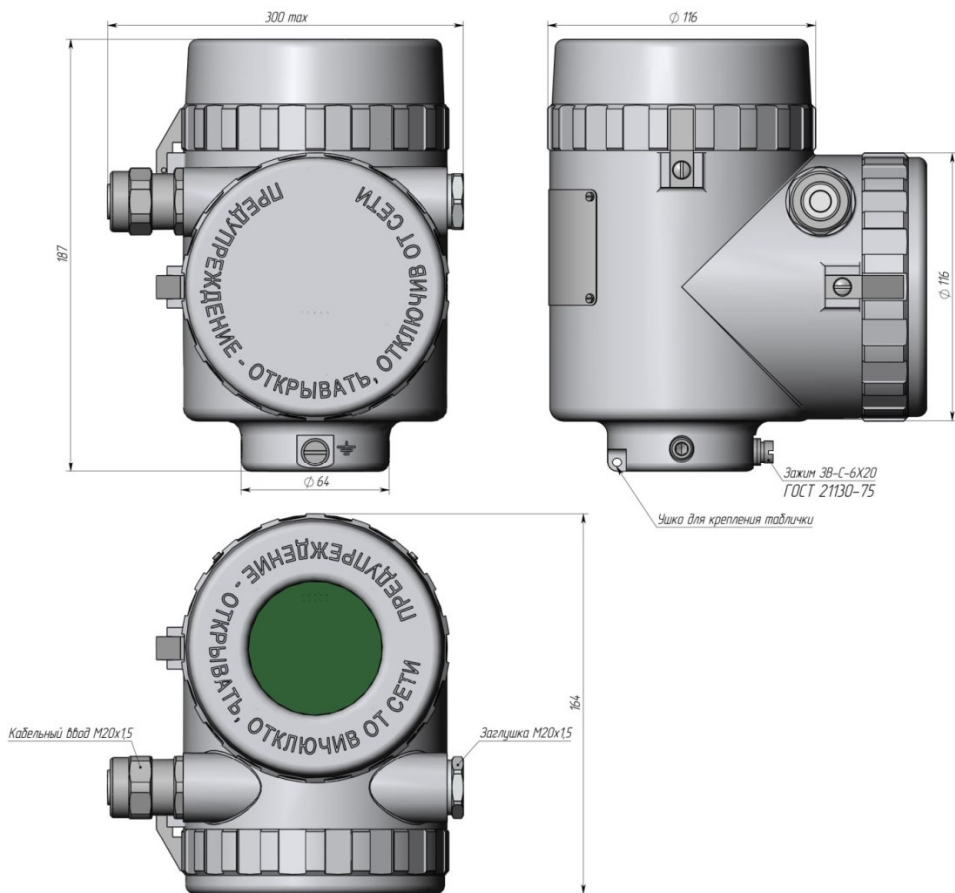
Габаритные и установочные размеры алюминиевого корпуса блока электронного преобразователя. IP67. Дисплей сверху
